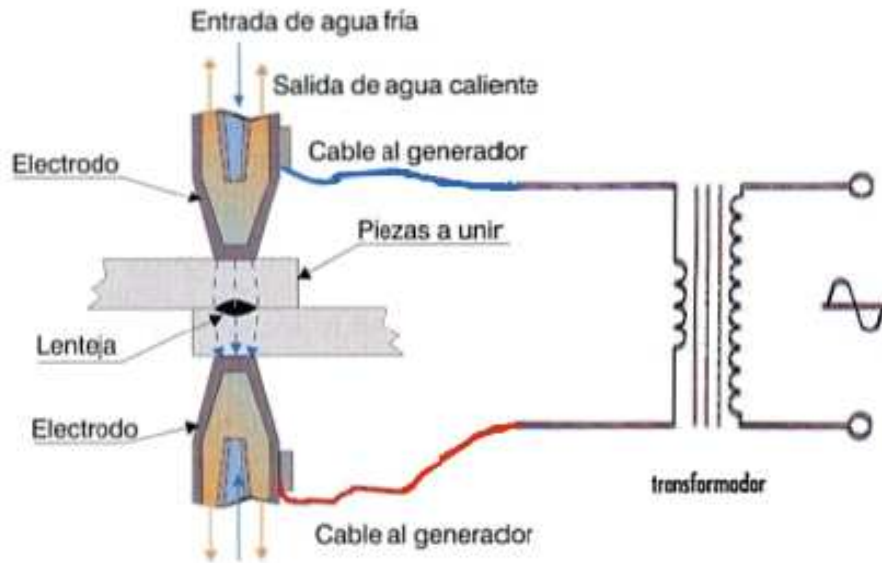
Circuito de soldadura por resistencia por puntos RSW
